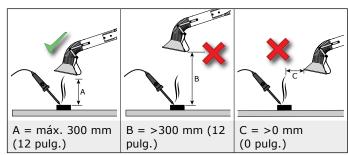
A = posición correcta de la campana (ejemplo: soldadura)
